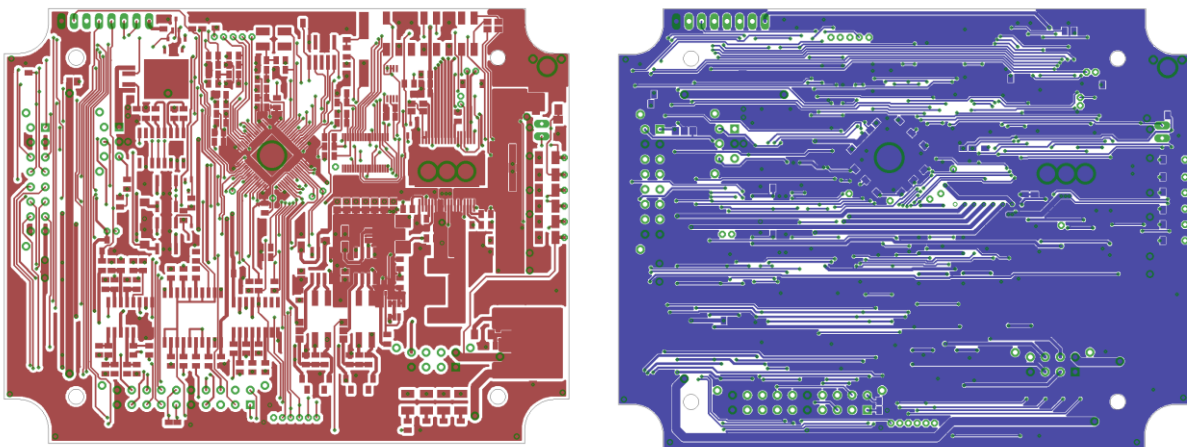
PCB Layout - Top und Bottom Seite
